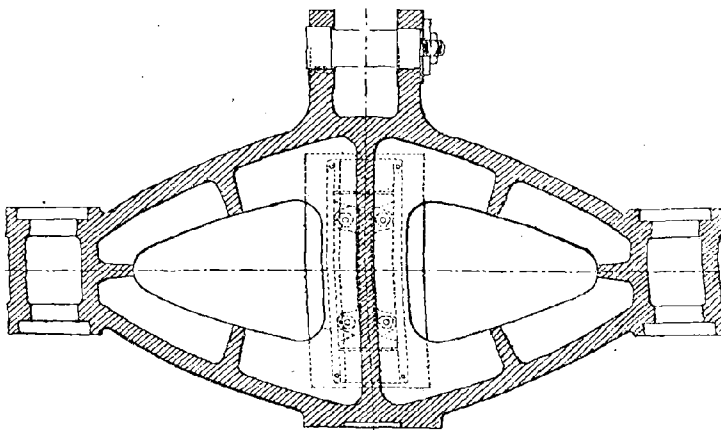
Crosse d'arrière d'un moteur Oechelhäuser.
